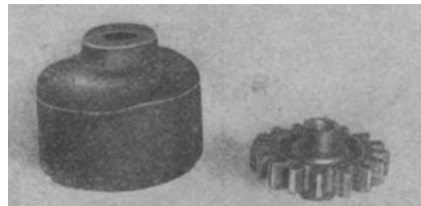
Durch Zerspanen aus dem Vollen gefertigtes Zahnrad.
